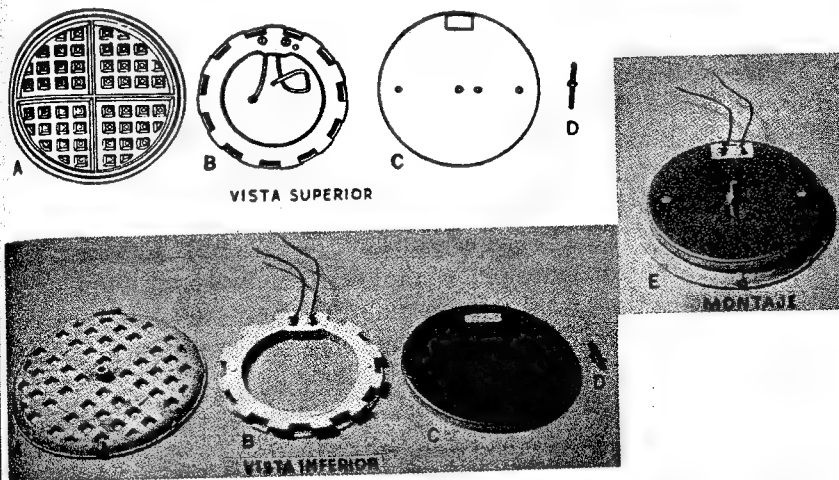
Piezas para el montaje del hornillo: A, pieza inferior de fundición de la parrilla; B, anillo de porcelana, submontaje; C, tapa de acero; D, pasador y tuerca; E, montaje de las piezas A, B, C y D.
